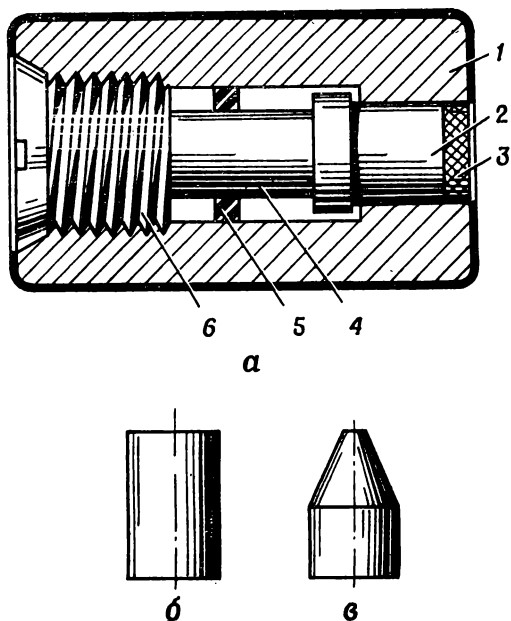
Измерение давления пороховых газов: а) вкладной крешерный прибор; б) цилиндрический крешерный столбик; в) конический крешерный столбик;
